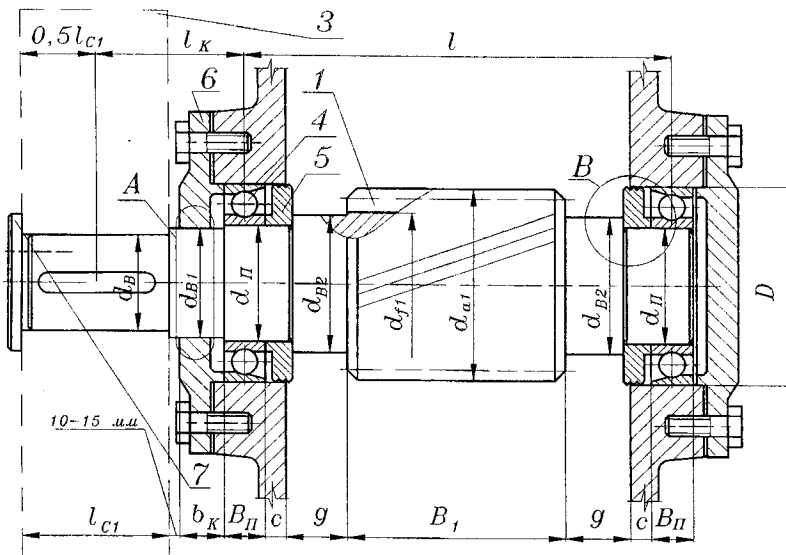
Вал-шестерня косозубої циліндричної передачі
